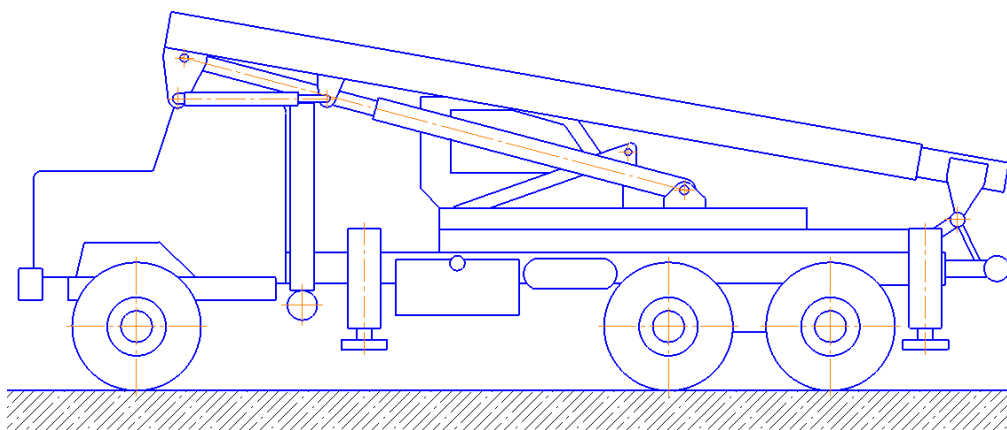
Аварийно-спасательный агрегат в транспортном положении
